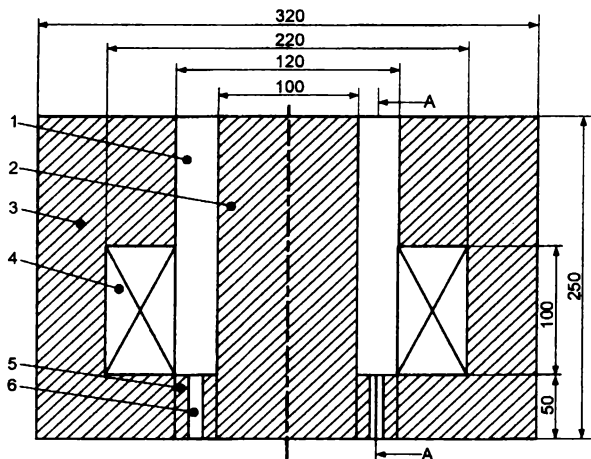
Эскиз погружного нагревателя-перемешивателя:
